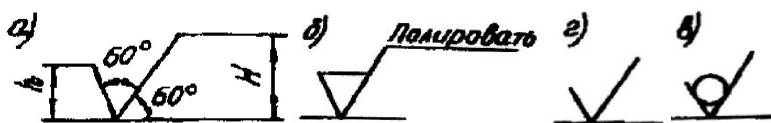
Виды знаков условного обозначения шероховатости поверхности на чертеже детали
